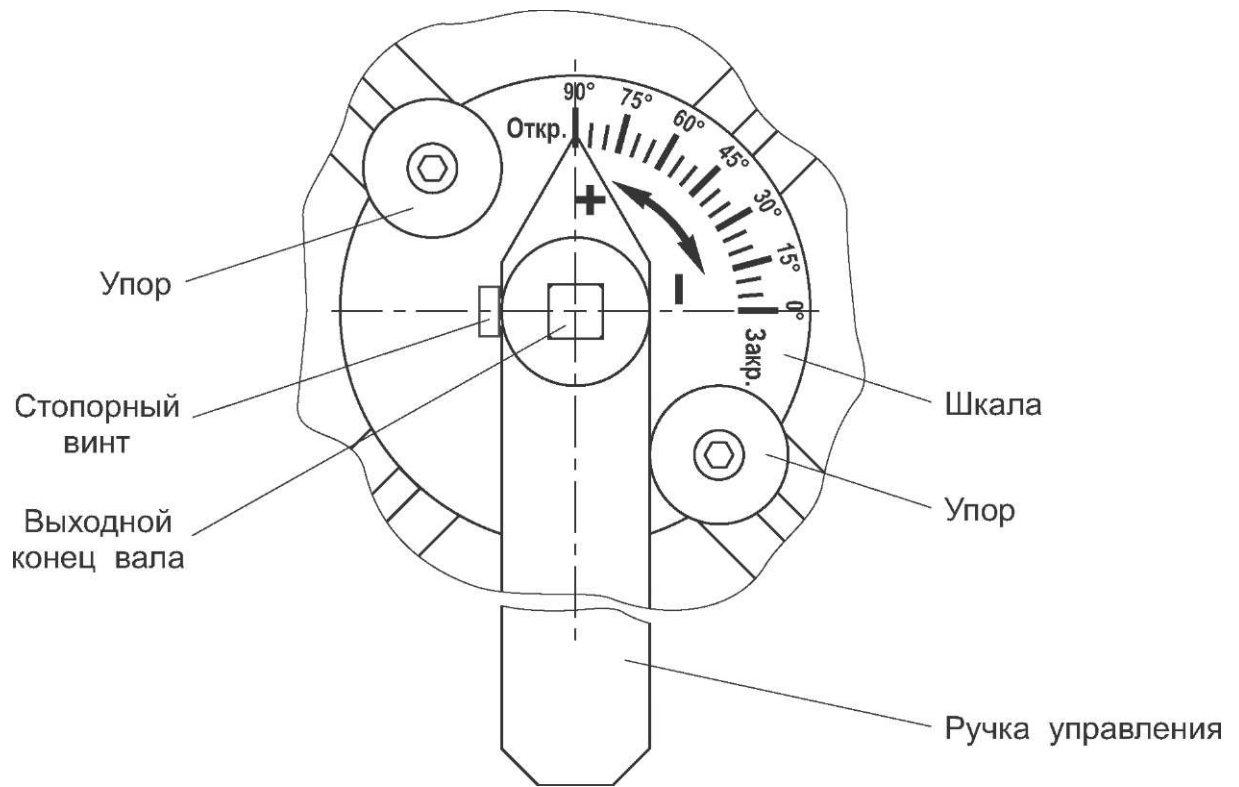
Заслонка регулирующая с ручным управлением (вид сверху)
